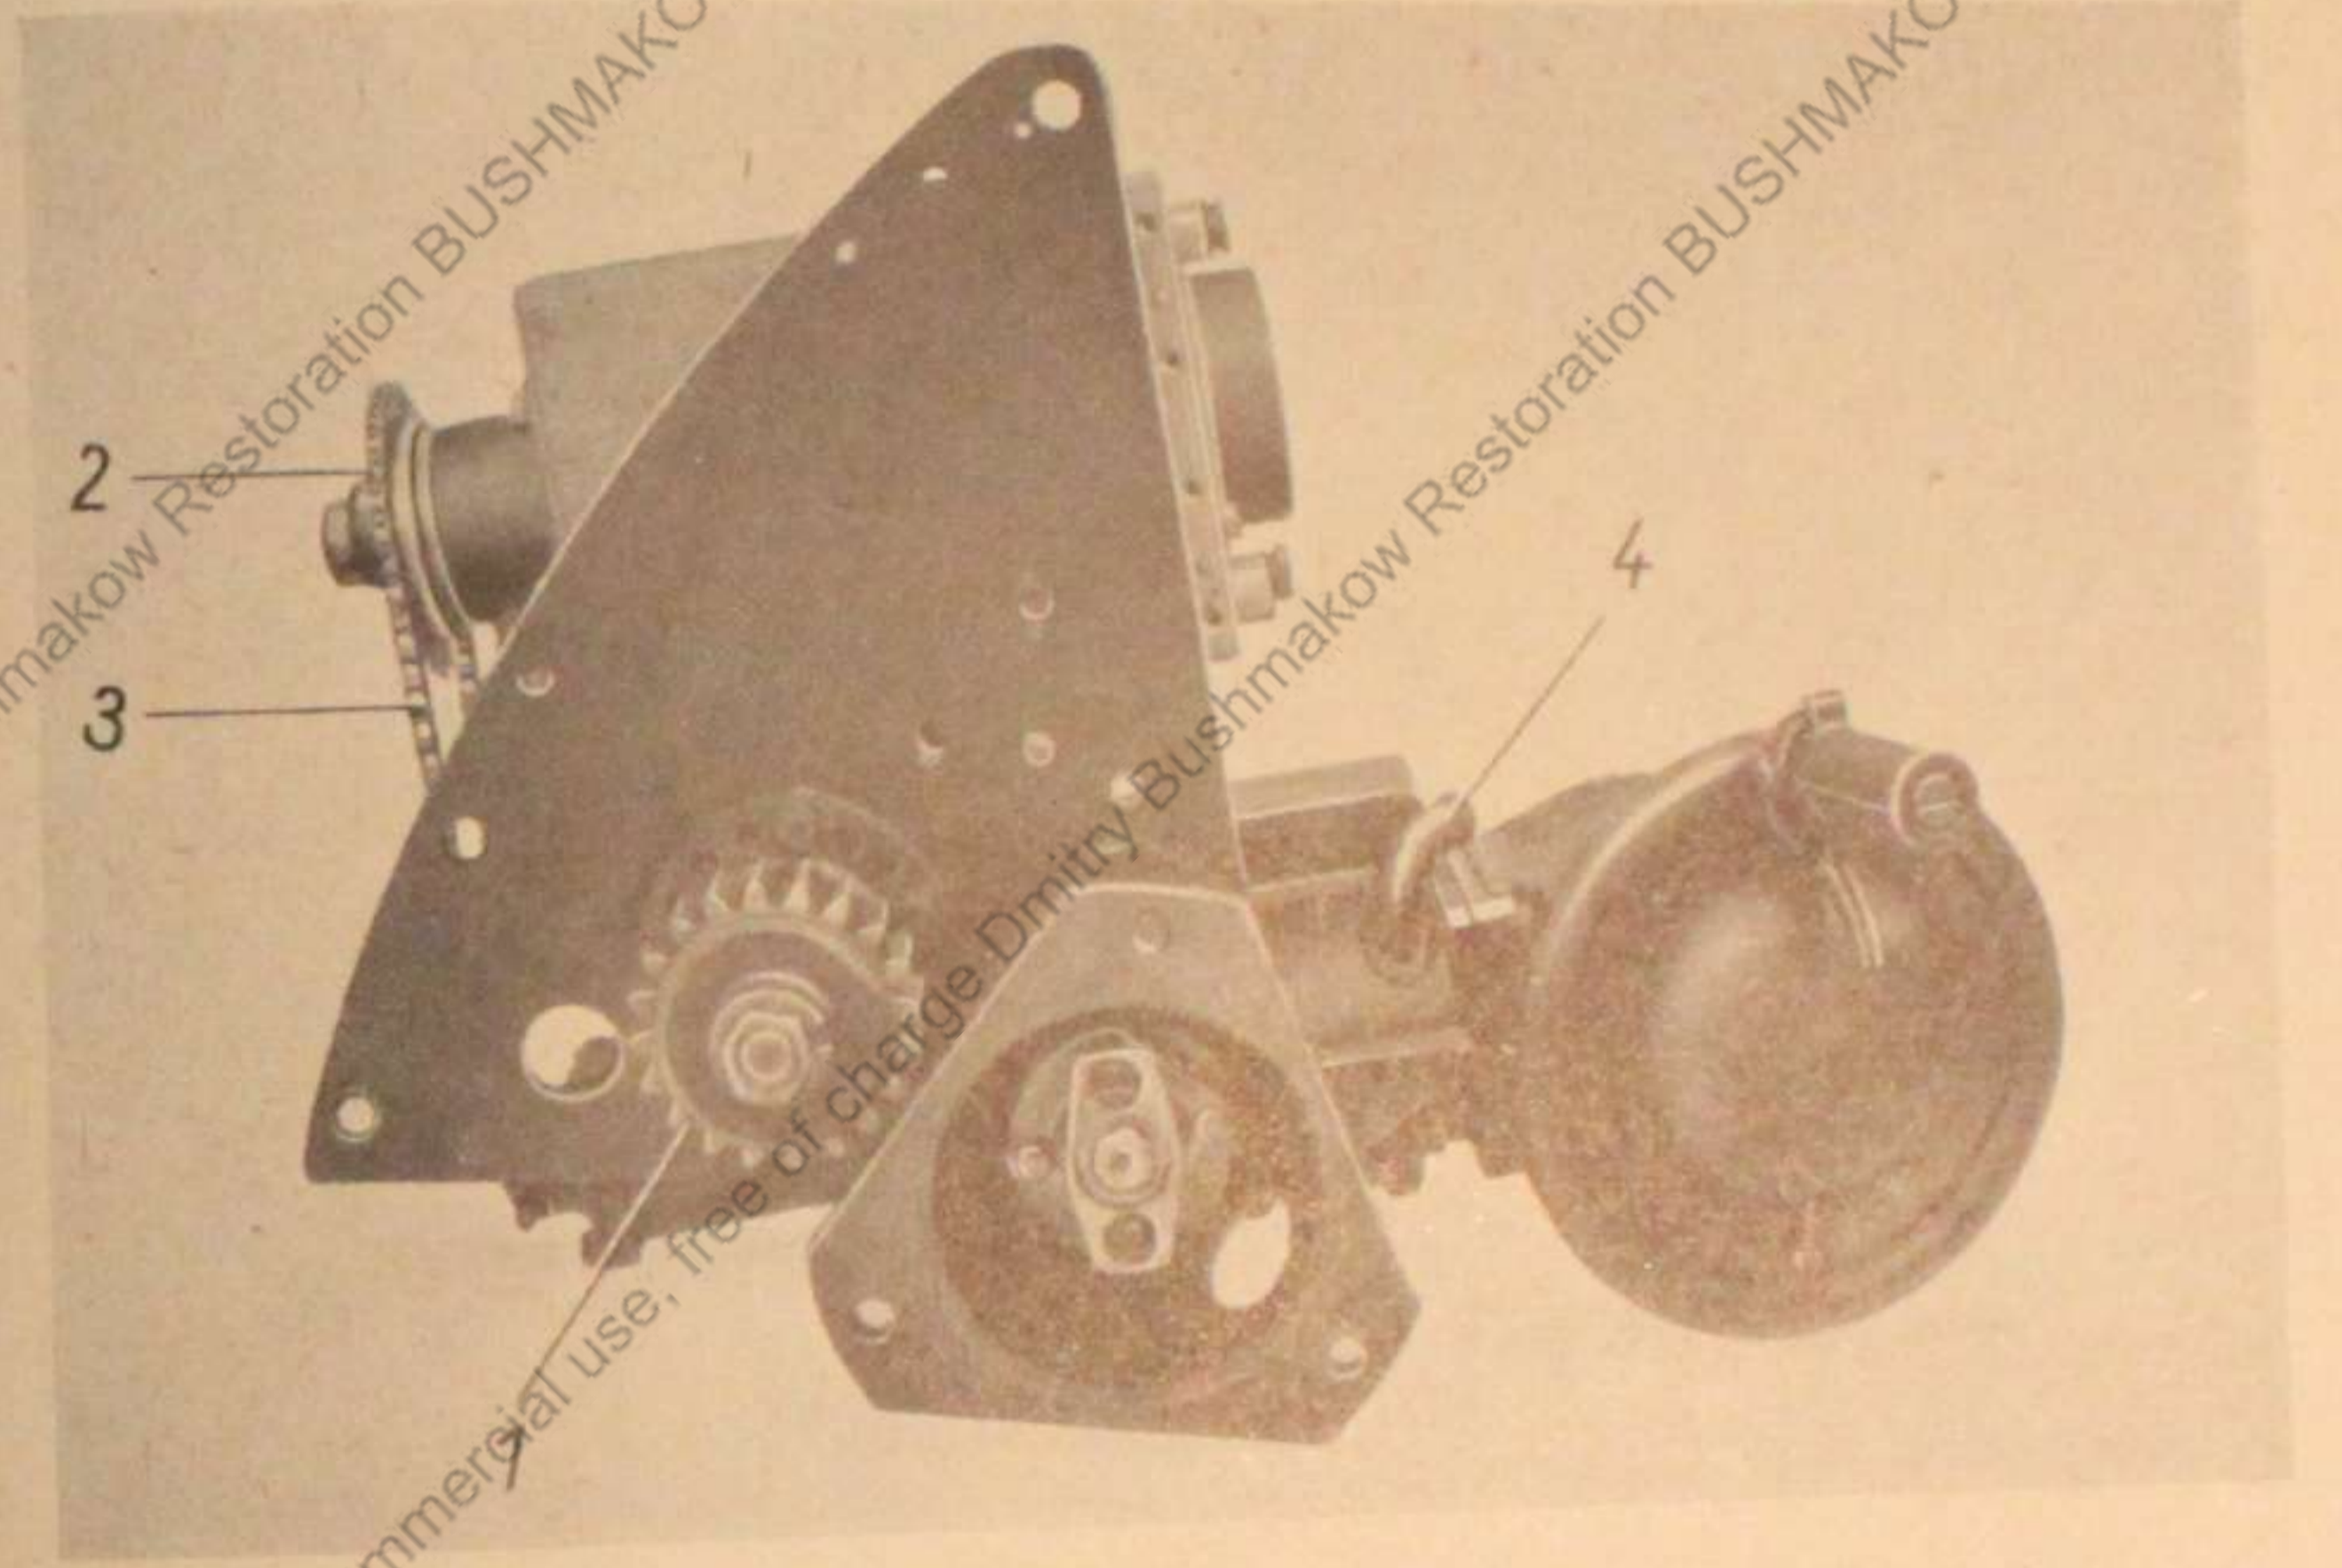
Turmschwenkwerk, ohne Schwenkmotor (von unten)
